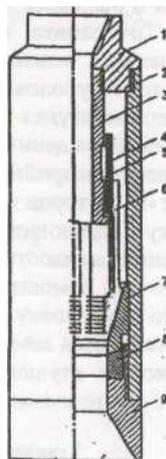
Труболовка наружная освобождающаяся (ТНП): 1-переводник; 2-корпус; 3-шпиндель; 4-втулка; 5-шпонка; 6-цанга; 7-конус; 8-уплотнительный элемент; 9-воронка
